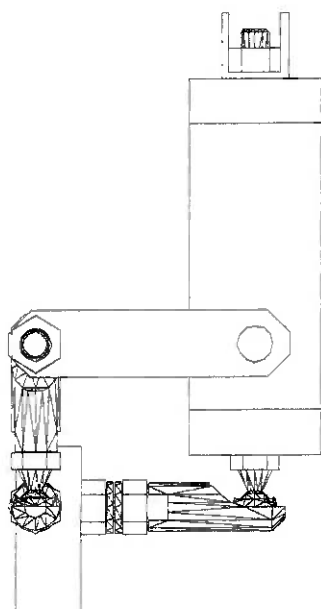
Desenho de conjunto do joelho - vista frontal
